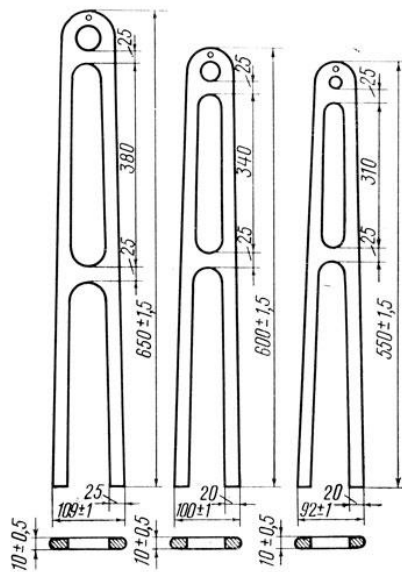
Правилка для шкурок соболя конструкции Ю.В. Игнатова
